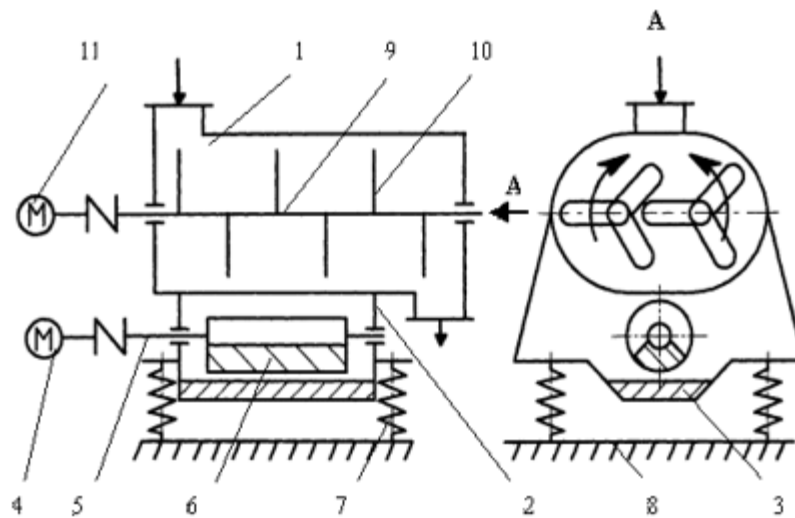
Схема двовального віброзмішувача типу ДВС–Н: 1 – камера змішування; 2 – кронштейни; 3 – противага; 4 – електродвигун приводу вала вібратора; 5 – вал вібратора; 6 – дебаланс; 7 – пружини; 8 – рама; 9 – вал; 10 – лопаті; 11 – електродвигун приводу лопатевих валів
